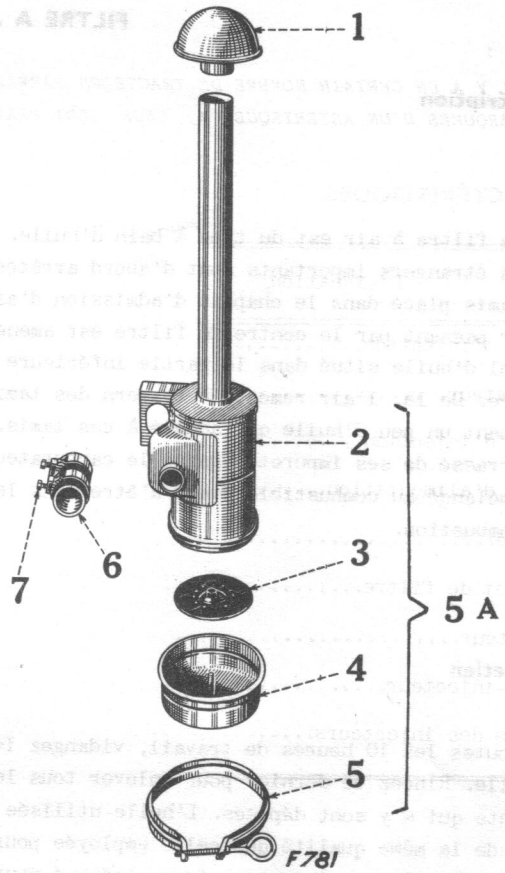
Vue éclatée du filtre à air. 1 - Chapeau d'admission d'air au filtre. 2 - Corps du filtre. 3 - Déflecteur. 4 - Bol du filtre à air. 5 - Collier de fixation du bol d'huile. 5A - Filtre à air complet. 6 - Tuyau flexible du filtre à air. 7 - Collier de serrage du tuyau flexible.
